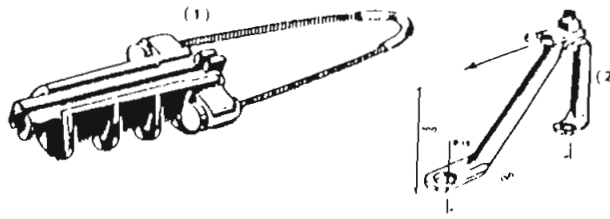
Conjunto de anclaje para redes tendidas sobre fachadas
